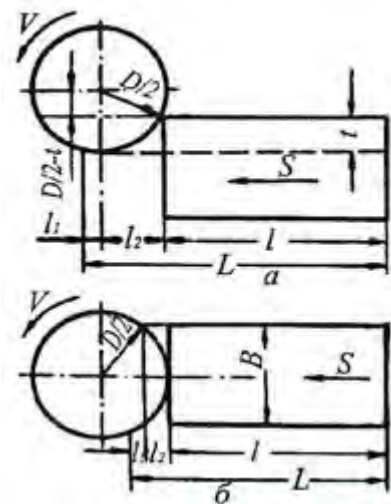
Схеми для визначення довжини врізання фрези при циліндричному (а) і торцевому (б) фрезеруванні
